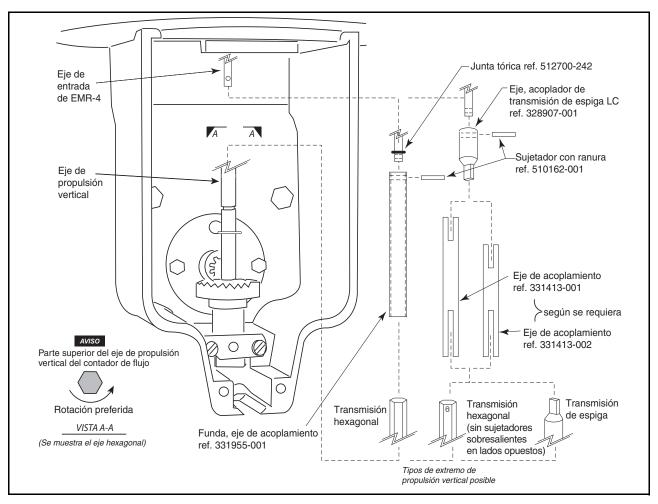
Instalación del acoplamiento del adaptador del codificador del contador
